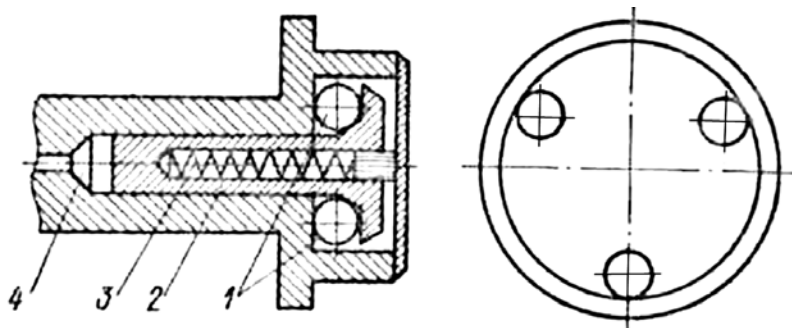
Устройство для автоматической балансировки круга на станке
